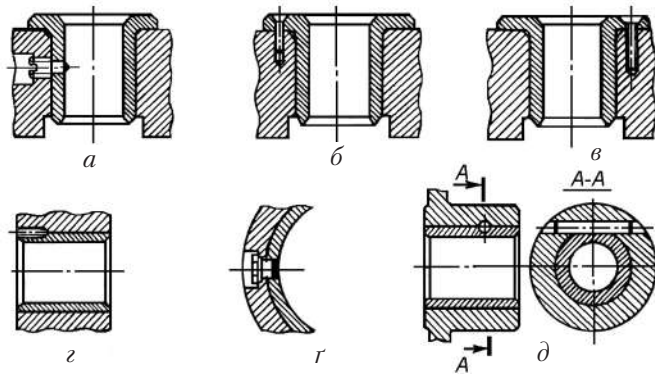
Способи закріплення втулок у корпусі підшипника:
